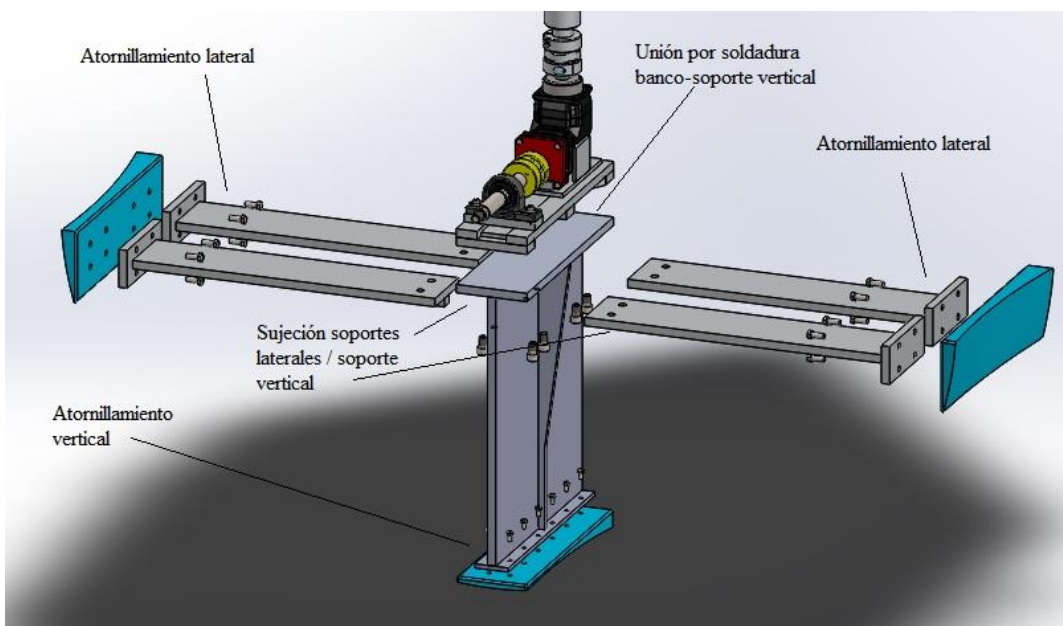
13. Explosionado del ensamblaje de los soportes. Fuente: diseño propio.
